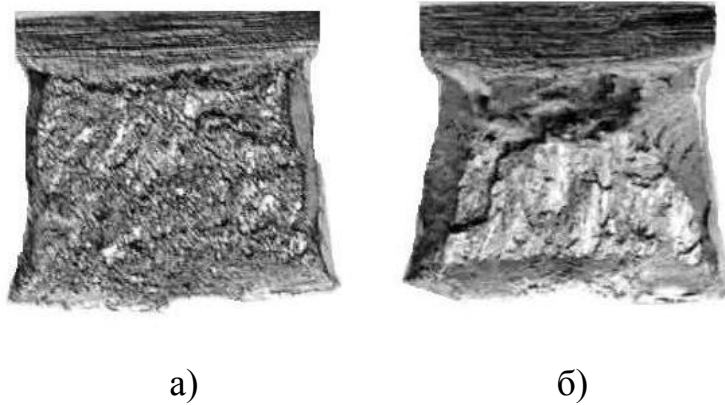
Изломы ударных образцов металла шва после испытания при +20°C: а) – без термической обработки после сварки; б) – с высоким отпуском после сварки (x4)
